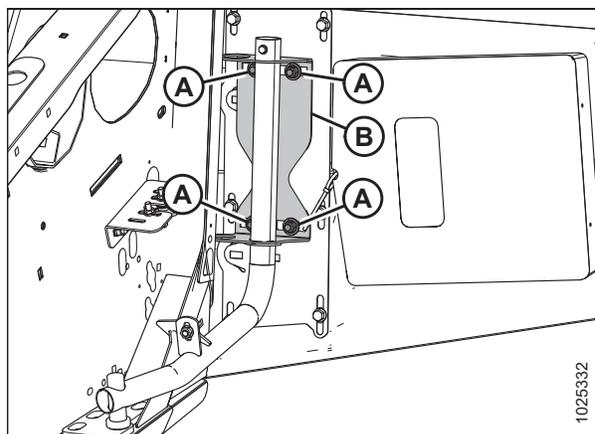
Tubo de suporte da tampa lateral esquerda
